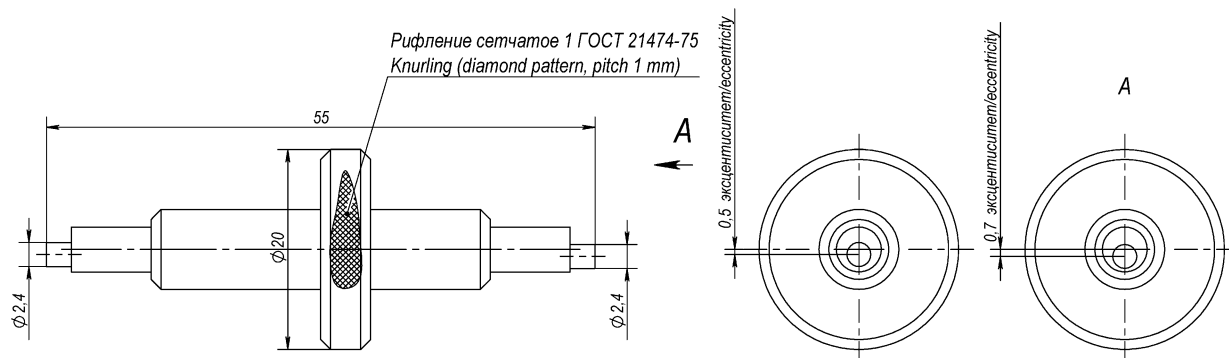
Приспособление для настройки неравномерности зазора EBKM.00D600.T7.00.000
